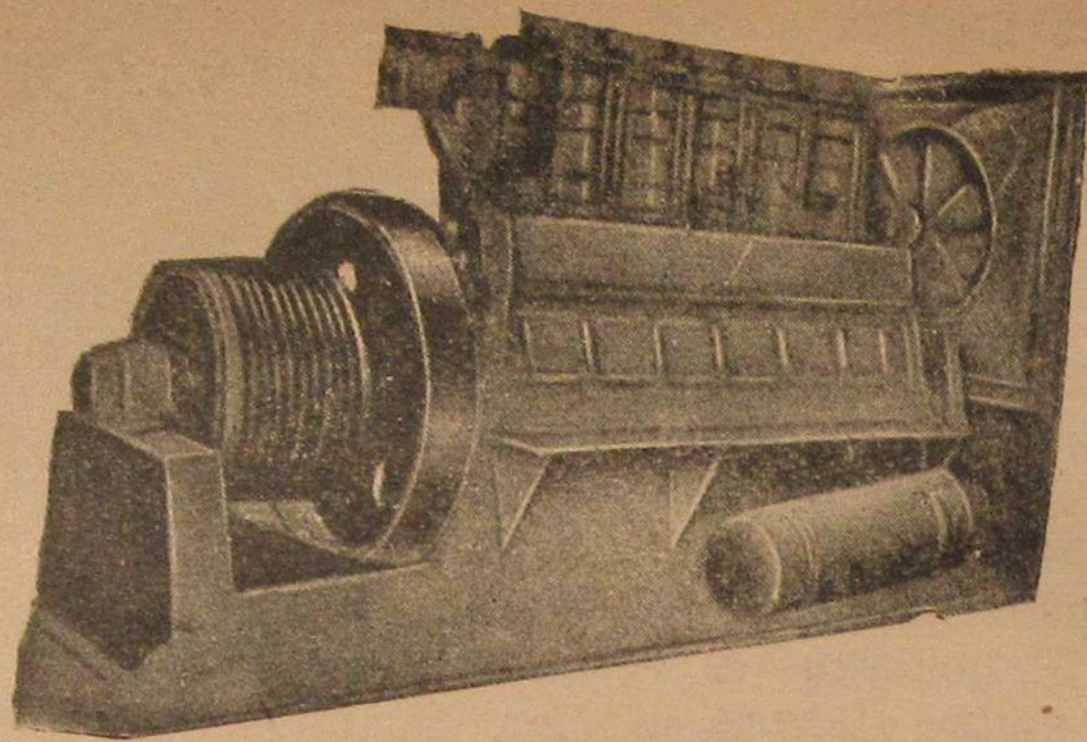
Шестицилиндровый комбинированный двигатель MAN мощностью в 650 л. с. Вид со стороны выхлопа.
